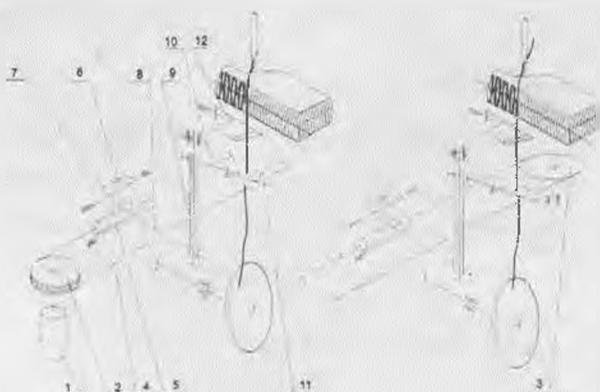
Кинематическая схема механизма автоматической обрезки ниток
